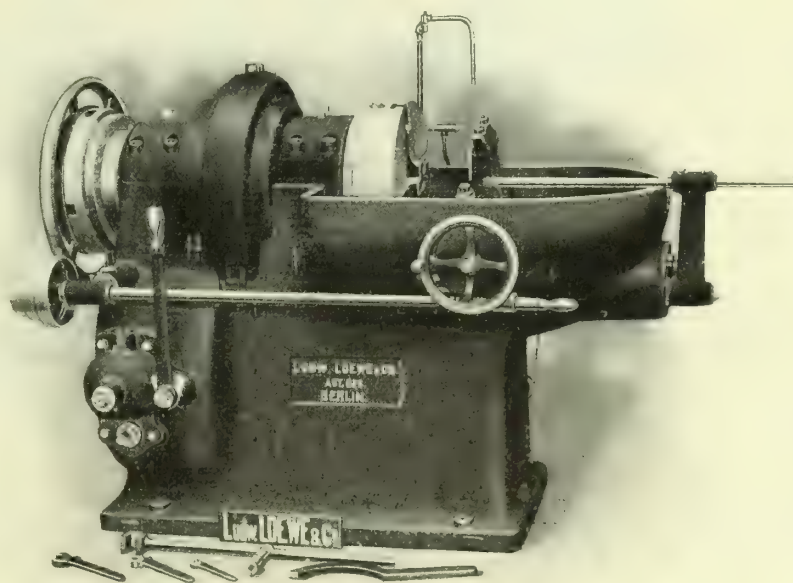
Abstechmaschine mit konstanter Schnitt-Geschwindigkeit
